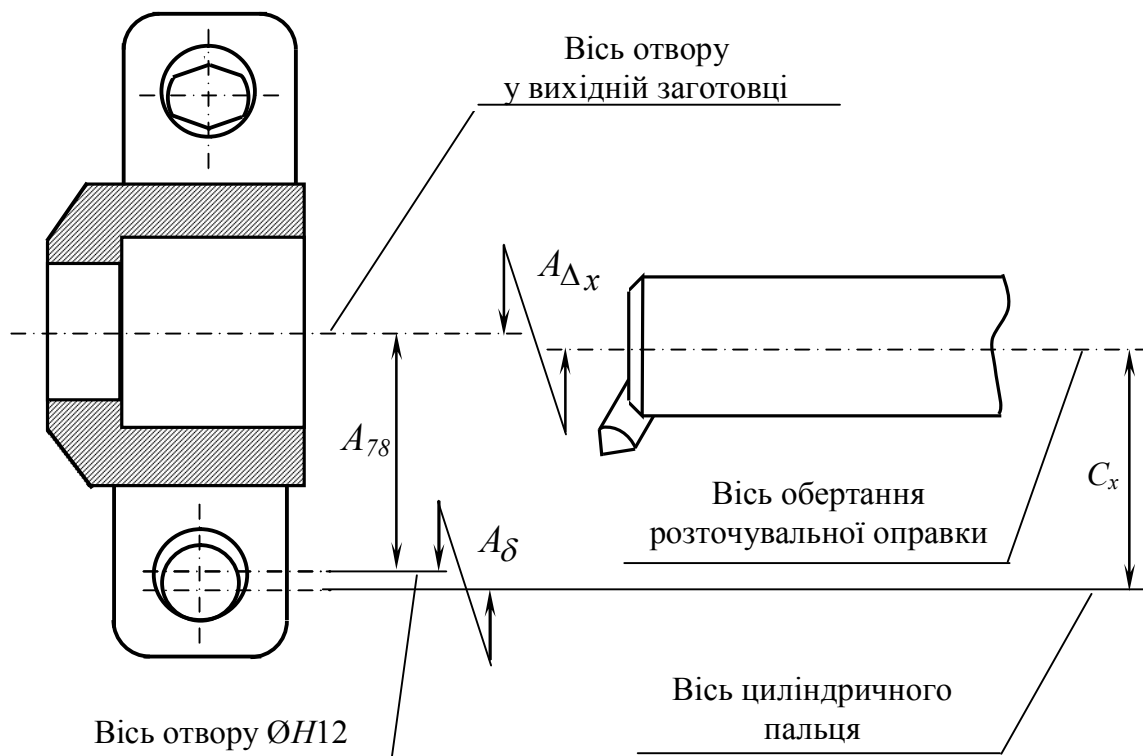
Схема розмірного ланцюга для визначення похибки базування як складової мінімального припуску у напрямі осі  $X$
